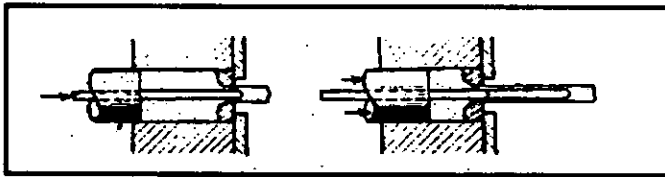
Extrusión de tubos con mandril móvil.(5)
